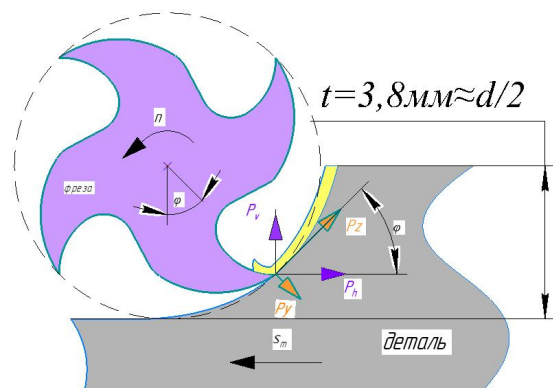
Составляющие силы (P_y , P_z), полученные после разложения силы при фрезеровании (P_h , P_v) на направление к оси фрезы и тангенциальное направление, т.е. касательно к направлению вращения фрезы (показано положение фрезы после заготовки на виде сверху)
